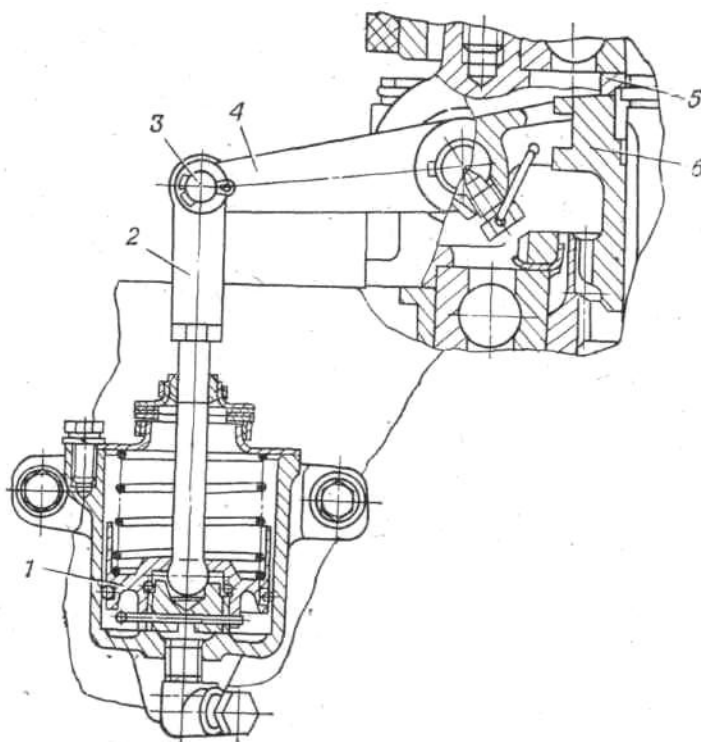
Регулировка механизма блокировки дифференциала раздаточной коробки:
